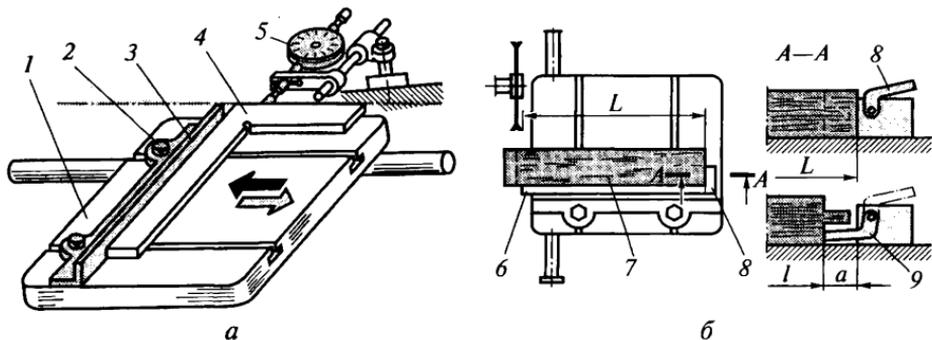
Настройка каретки одностороннего рамного шипорезного станка: *a* — крепление направляющей линейки; *б* — установка упоров; 1 — каретка; 2 — болт; 3 — направляющая линейка; 4 — поверочный угольник; 5 — индикатор; 6 — подпорный брусок; 7 — заготовка; 8 — неподвижный упор; 9 — откидной упор
